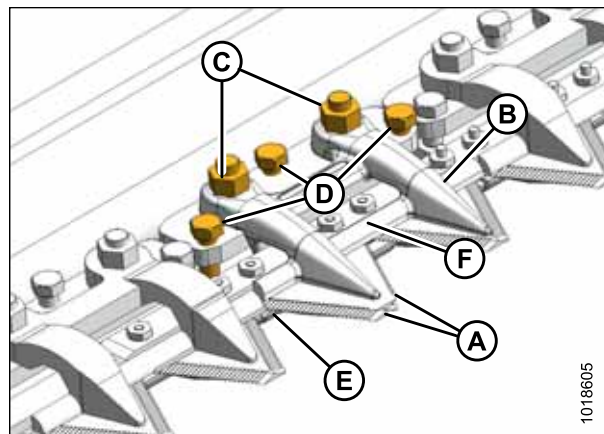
Центральный укороченный противорежущий палец двойного ножа
